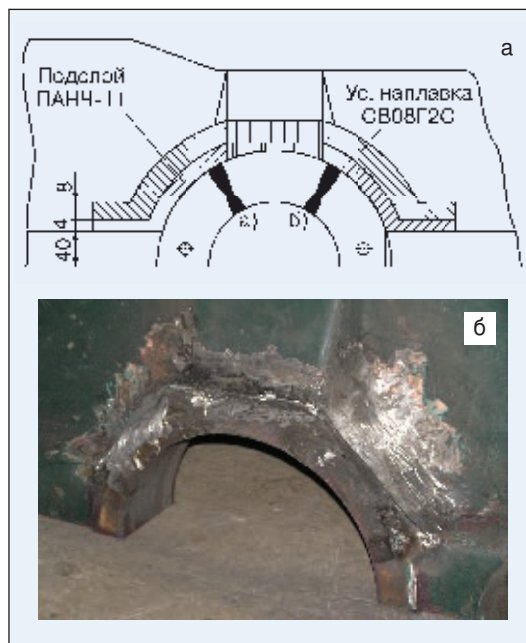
Схема нанесения (а) и общий вид (б) усиливающей наплавки
